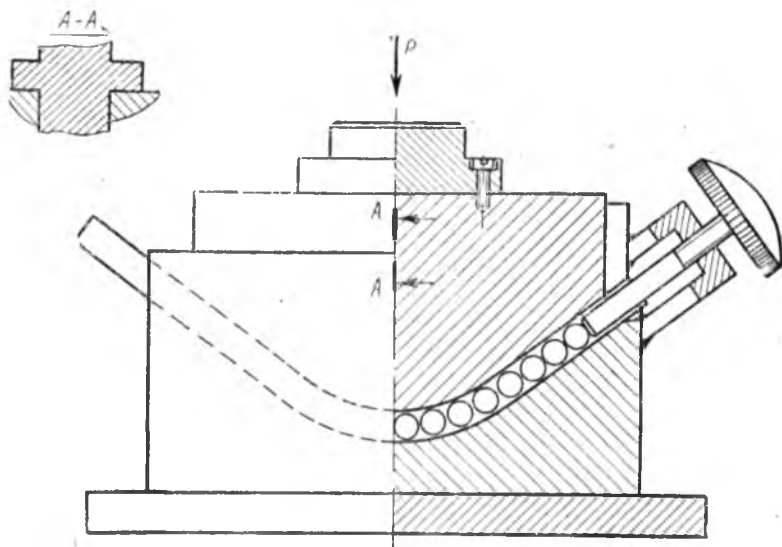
Винтовое приспособление для калибровки изогнутых волноводов с помощью роликов
